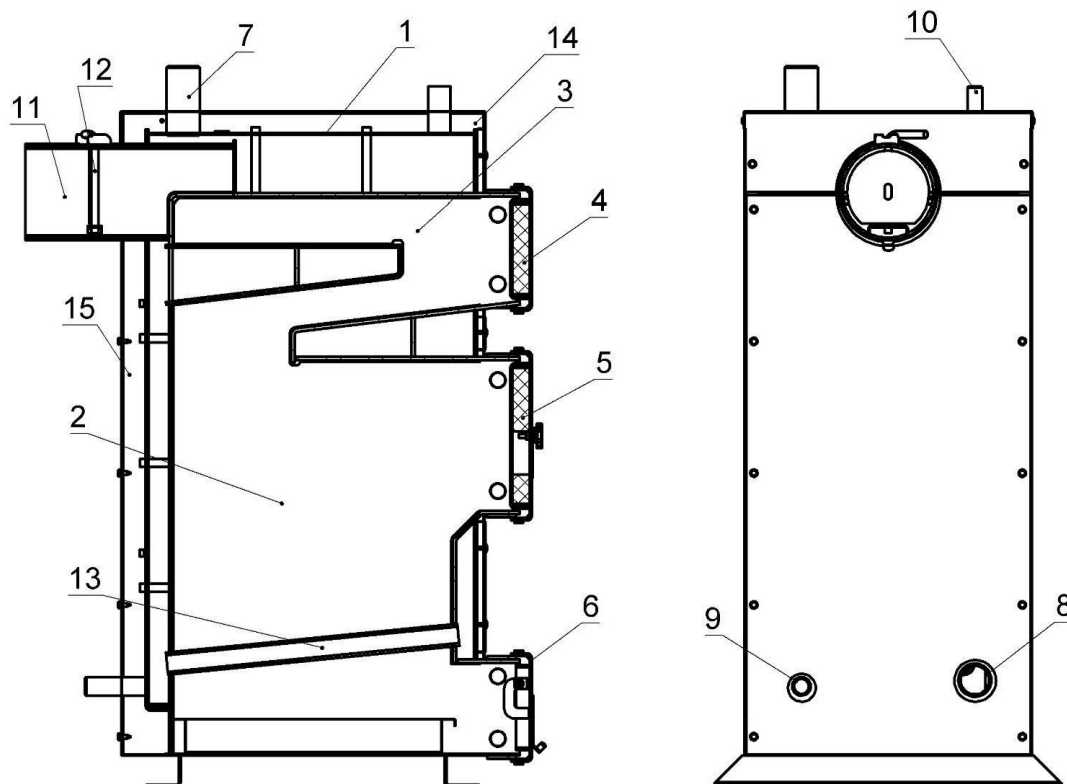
Внешний вид и основные элементы котла типа ГОРЫНЫЧ
